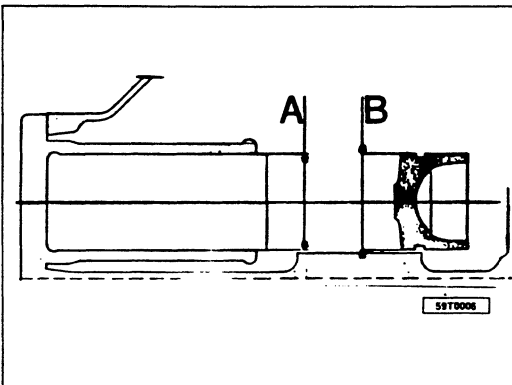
Diámetro del pistón y del cilindro de elevación.
